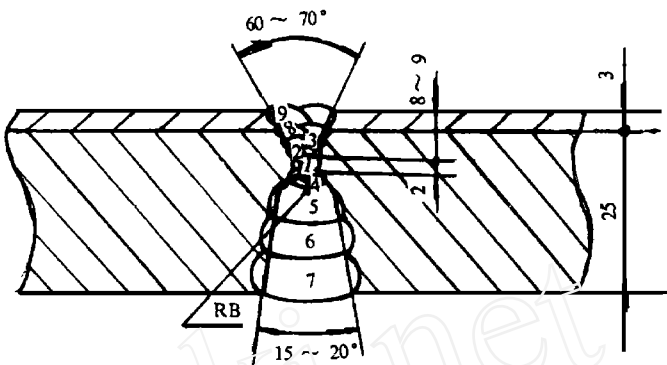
坡口形式、尺寸及焊接顺序(对接间隙3mm)
